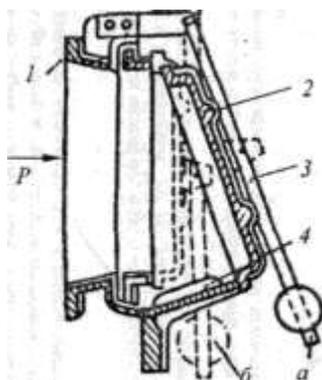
Предохранительный клапан с шарнирно-откидной дверцей: а-до взрыва; б-после взрыва; 1 - рама клапана; 2 - дверца (клапан); 3 - противовес; 4 - упор для фиксации клапана в исходном положении
